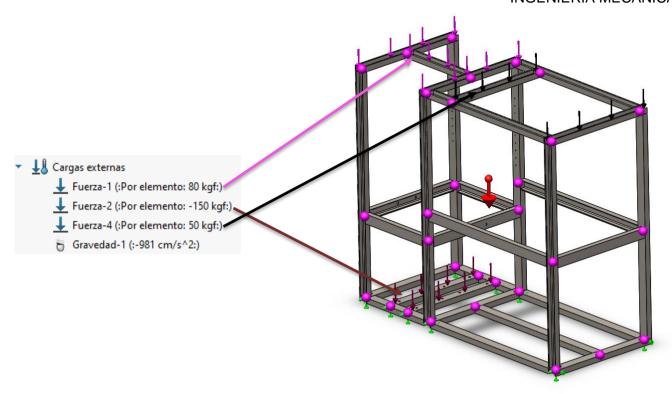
g: Cargas aplicadas en estructura.
